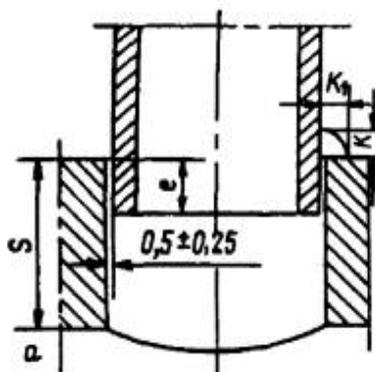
Рис. III – Угловой шов крепления трубок, с конструктивным зазором.
